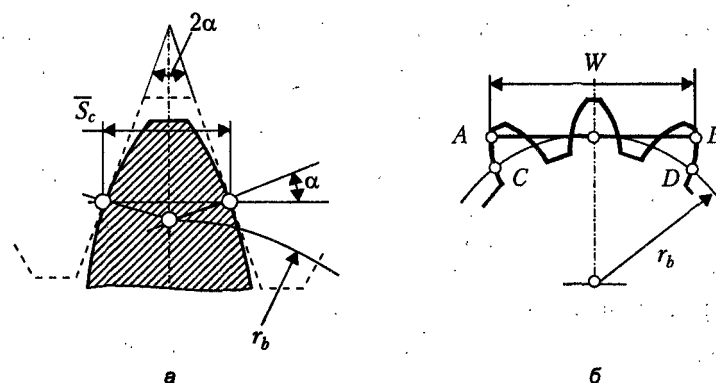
Параметры зубчатого колеса, влияющие на его кинематическую точность:
